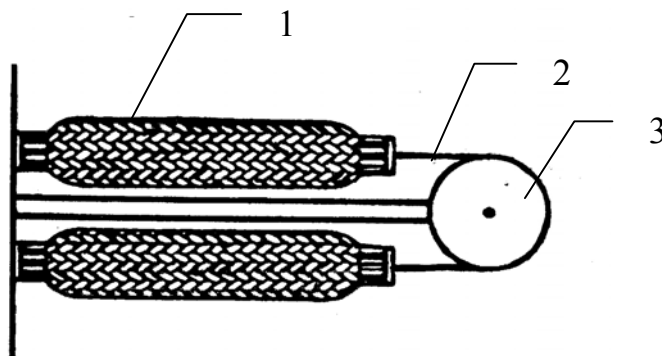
Реверсивный гибкий пневматический привод фирмы «Бриджестоун»:
